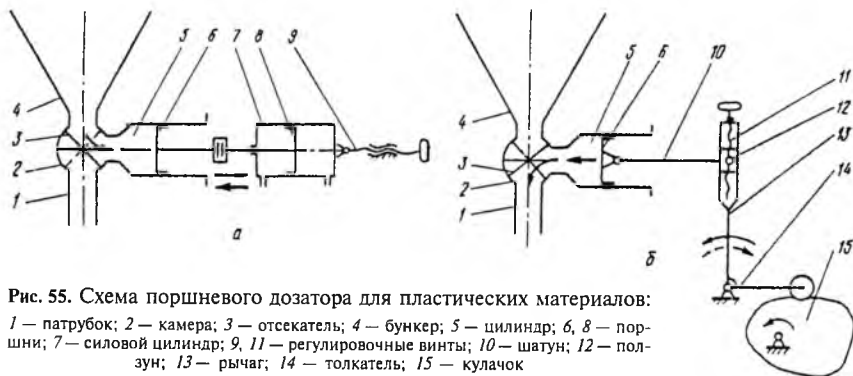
Схема поршневого дозатора для пластических материалов: 1 — патрубок; 2 — камера; 3 — отсекающий элемент; 4 — бункер; 5 — цилиндр; 6, 8 — поршни; 7 — силовой цилиндр; 9, 11 — регулировочные винты; 10 — шатун; 12 — ползун; 13 — рычаг; 14 — толкатель; 15 — кулачок
